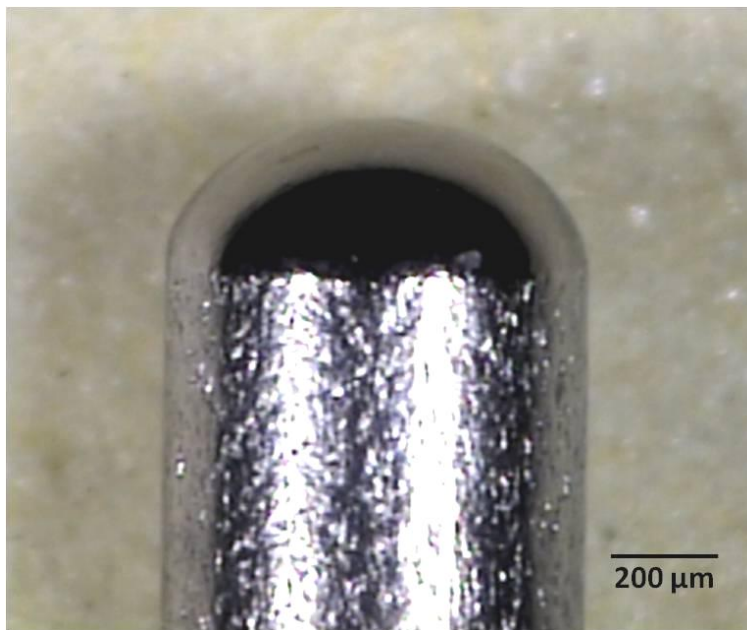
Referência da primeira solda aprovada no tubo de titânio
